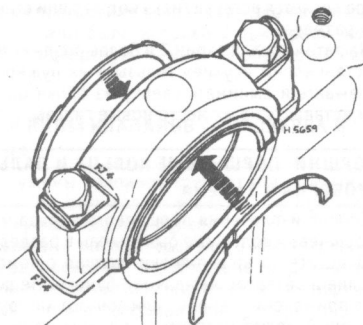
Упорные вкладыши коленчатого вала (см. раздел 21)
